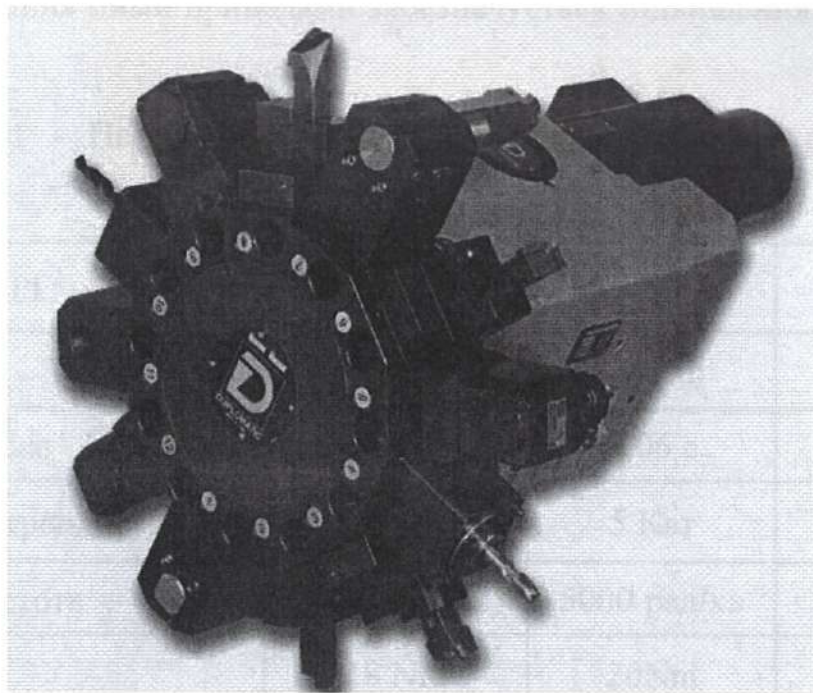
Револьверна головка токарних верстатів з одним приводом для повороту інструментального диска та осьового інструмента типу SM-BR 16.
